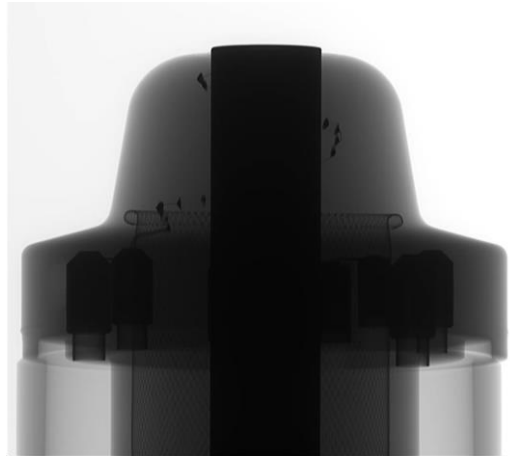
Vista em planta do perfil frontal do isolador 1 em RX.
